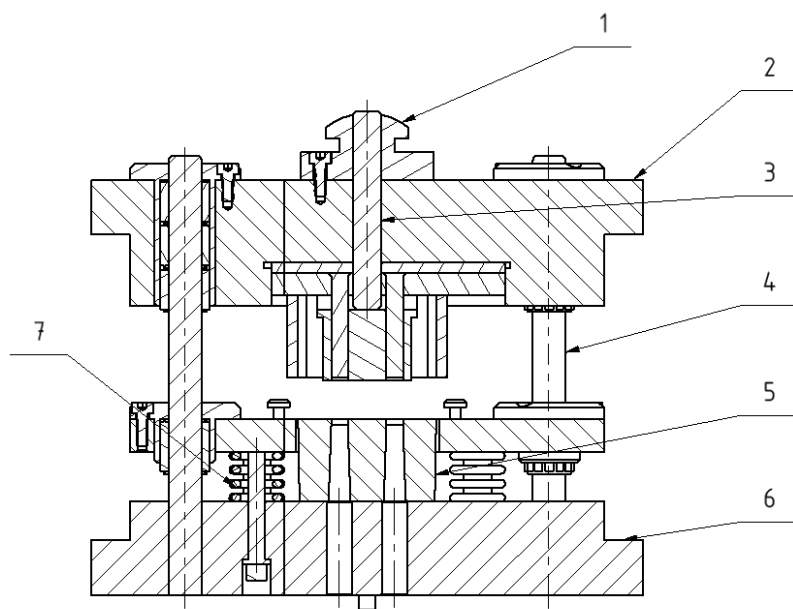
Ausstanzwerkzeug Komplettschnitt für Formplatte
